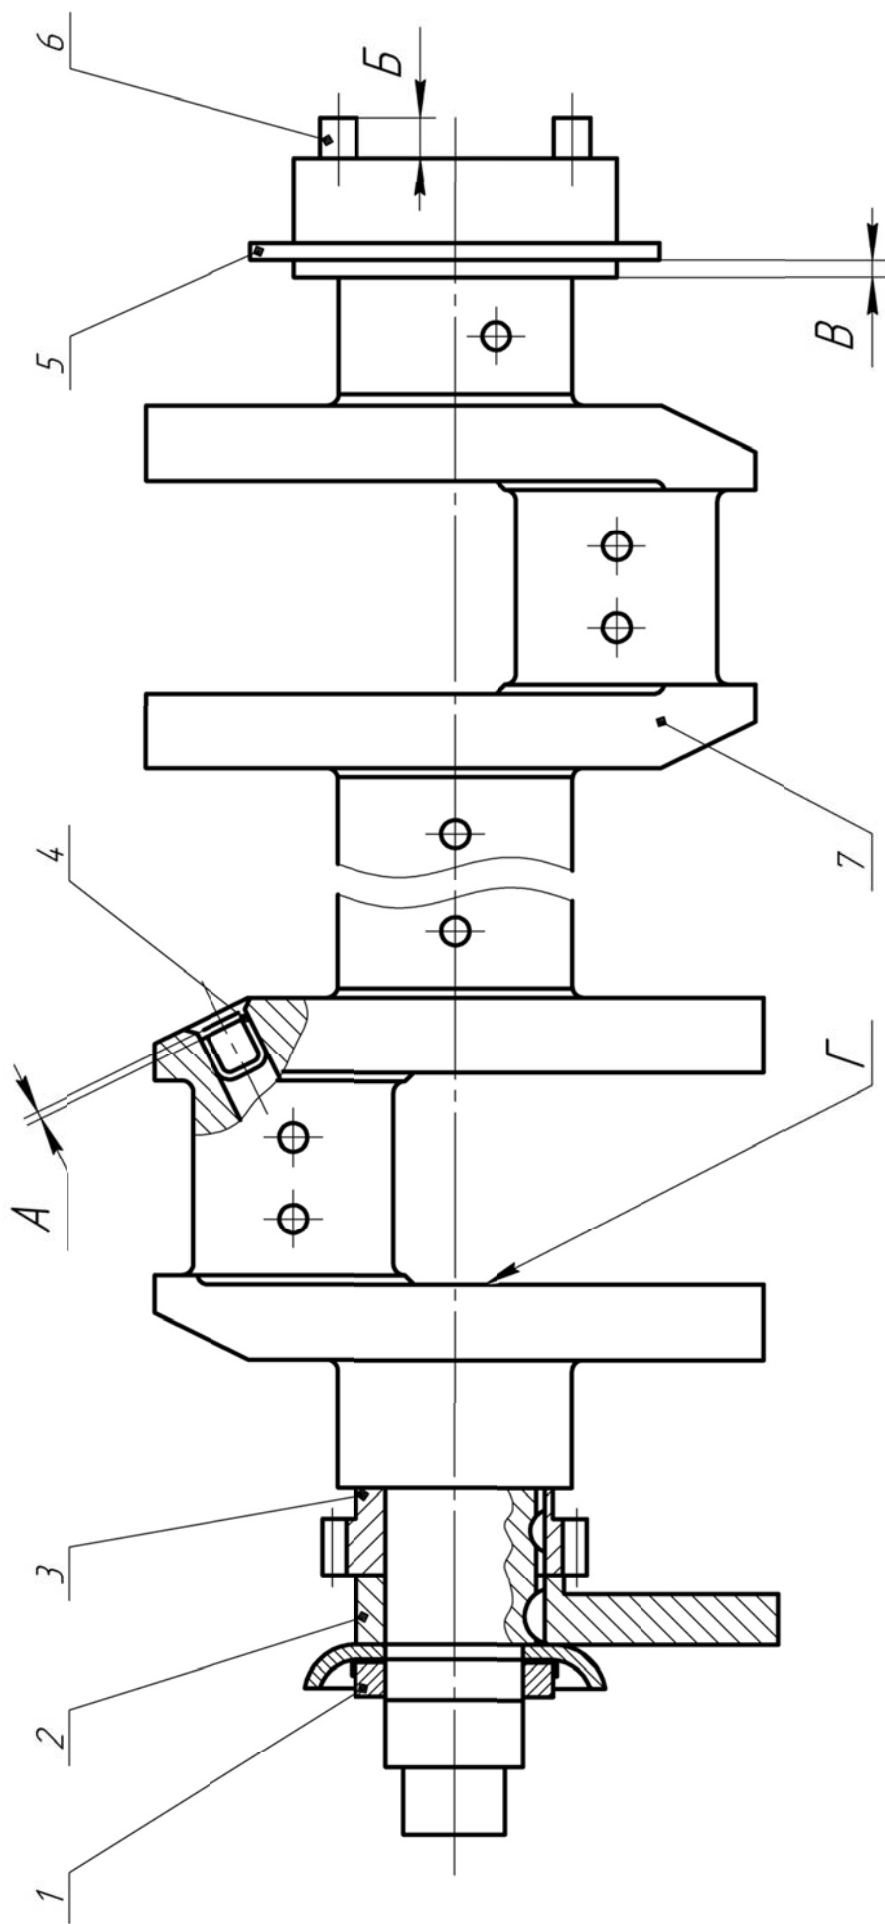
Вал коленчатый 238-1005008-Г2
